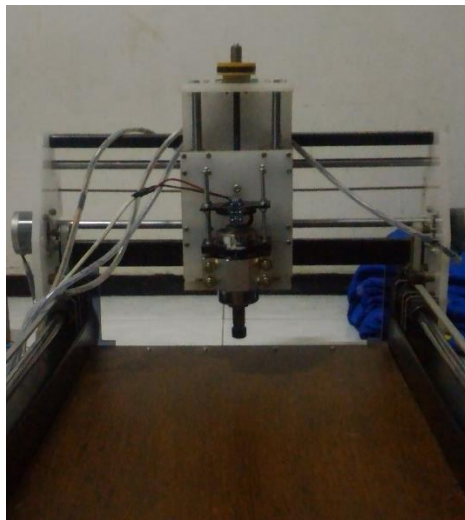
Motor *Stepper* Sumbu Y Tampak Samping Kiri
